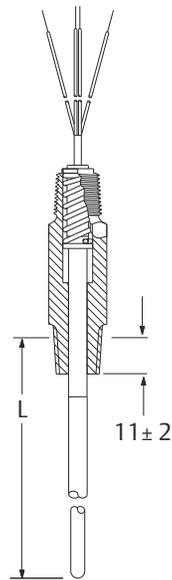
Universal-Rohrmontage mit Rosemount 3144P
